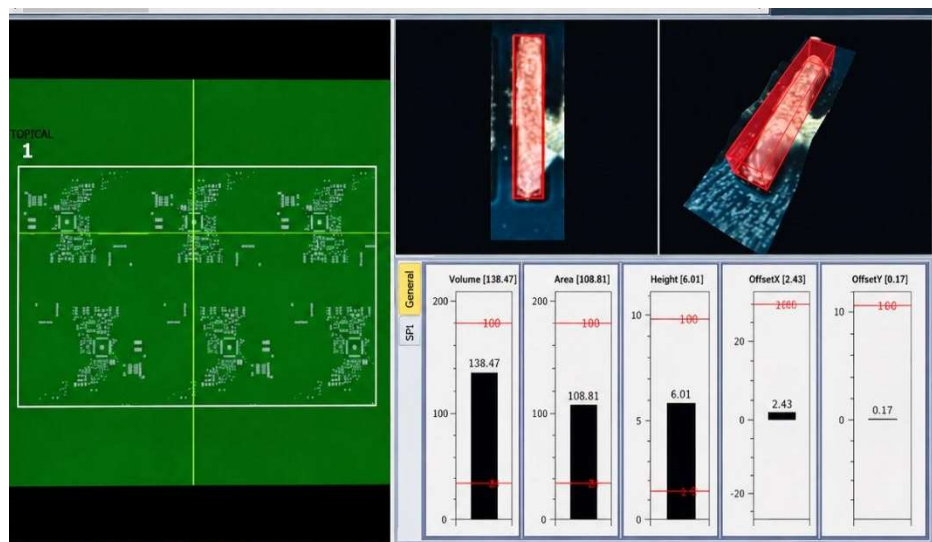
Defecto puente de soldadura detectado en SPI (bridge).
